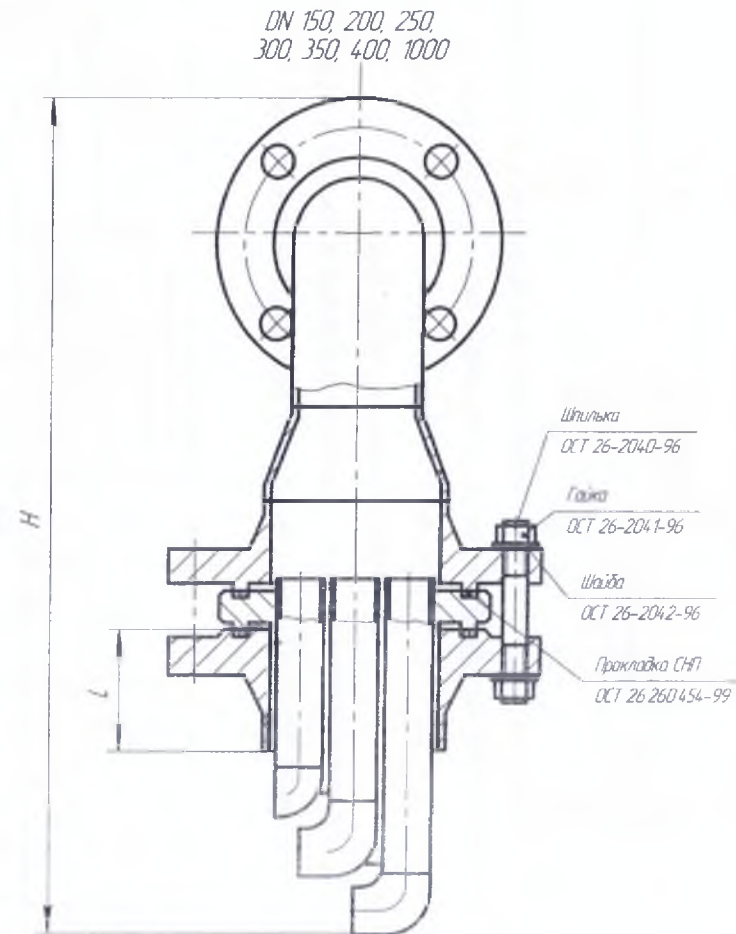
Устройство пробозаборное трубчатого типа
